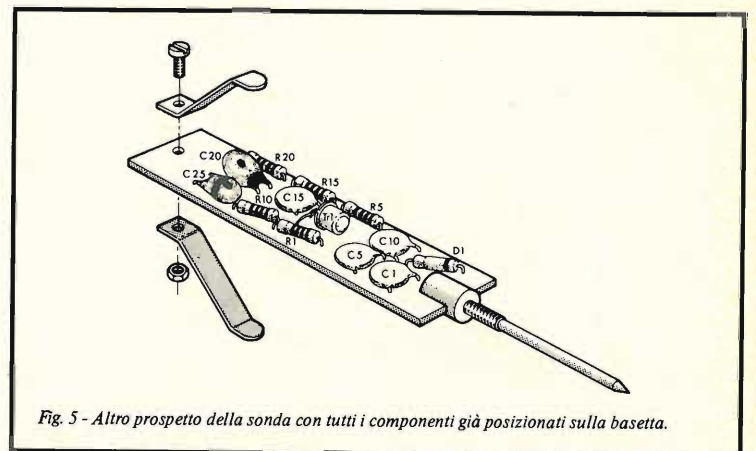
Altro prospetto della sonda con tutti i componenti già posizionati sulla basetta.
